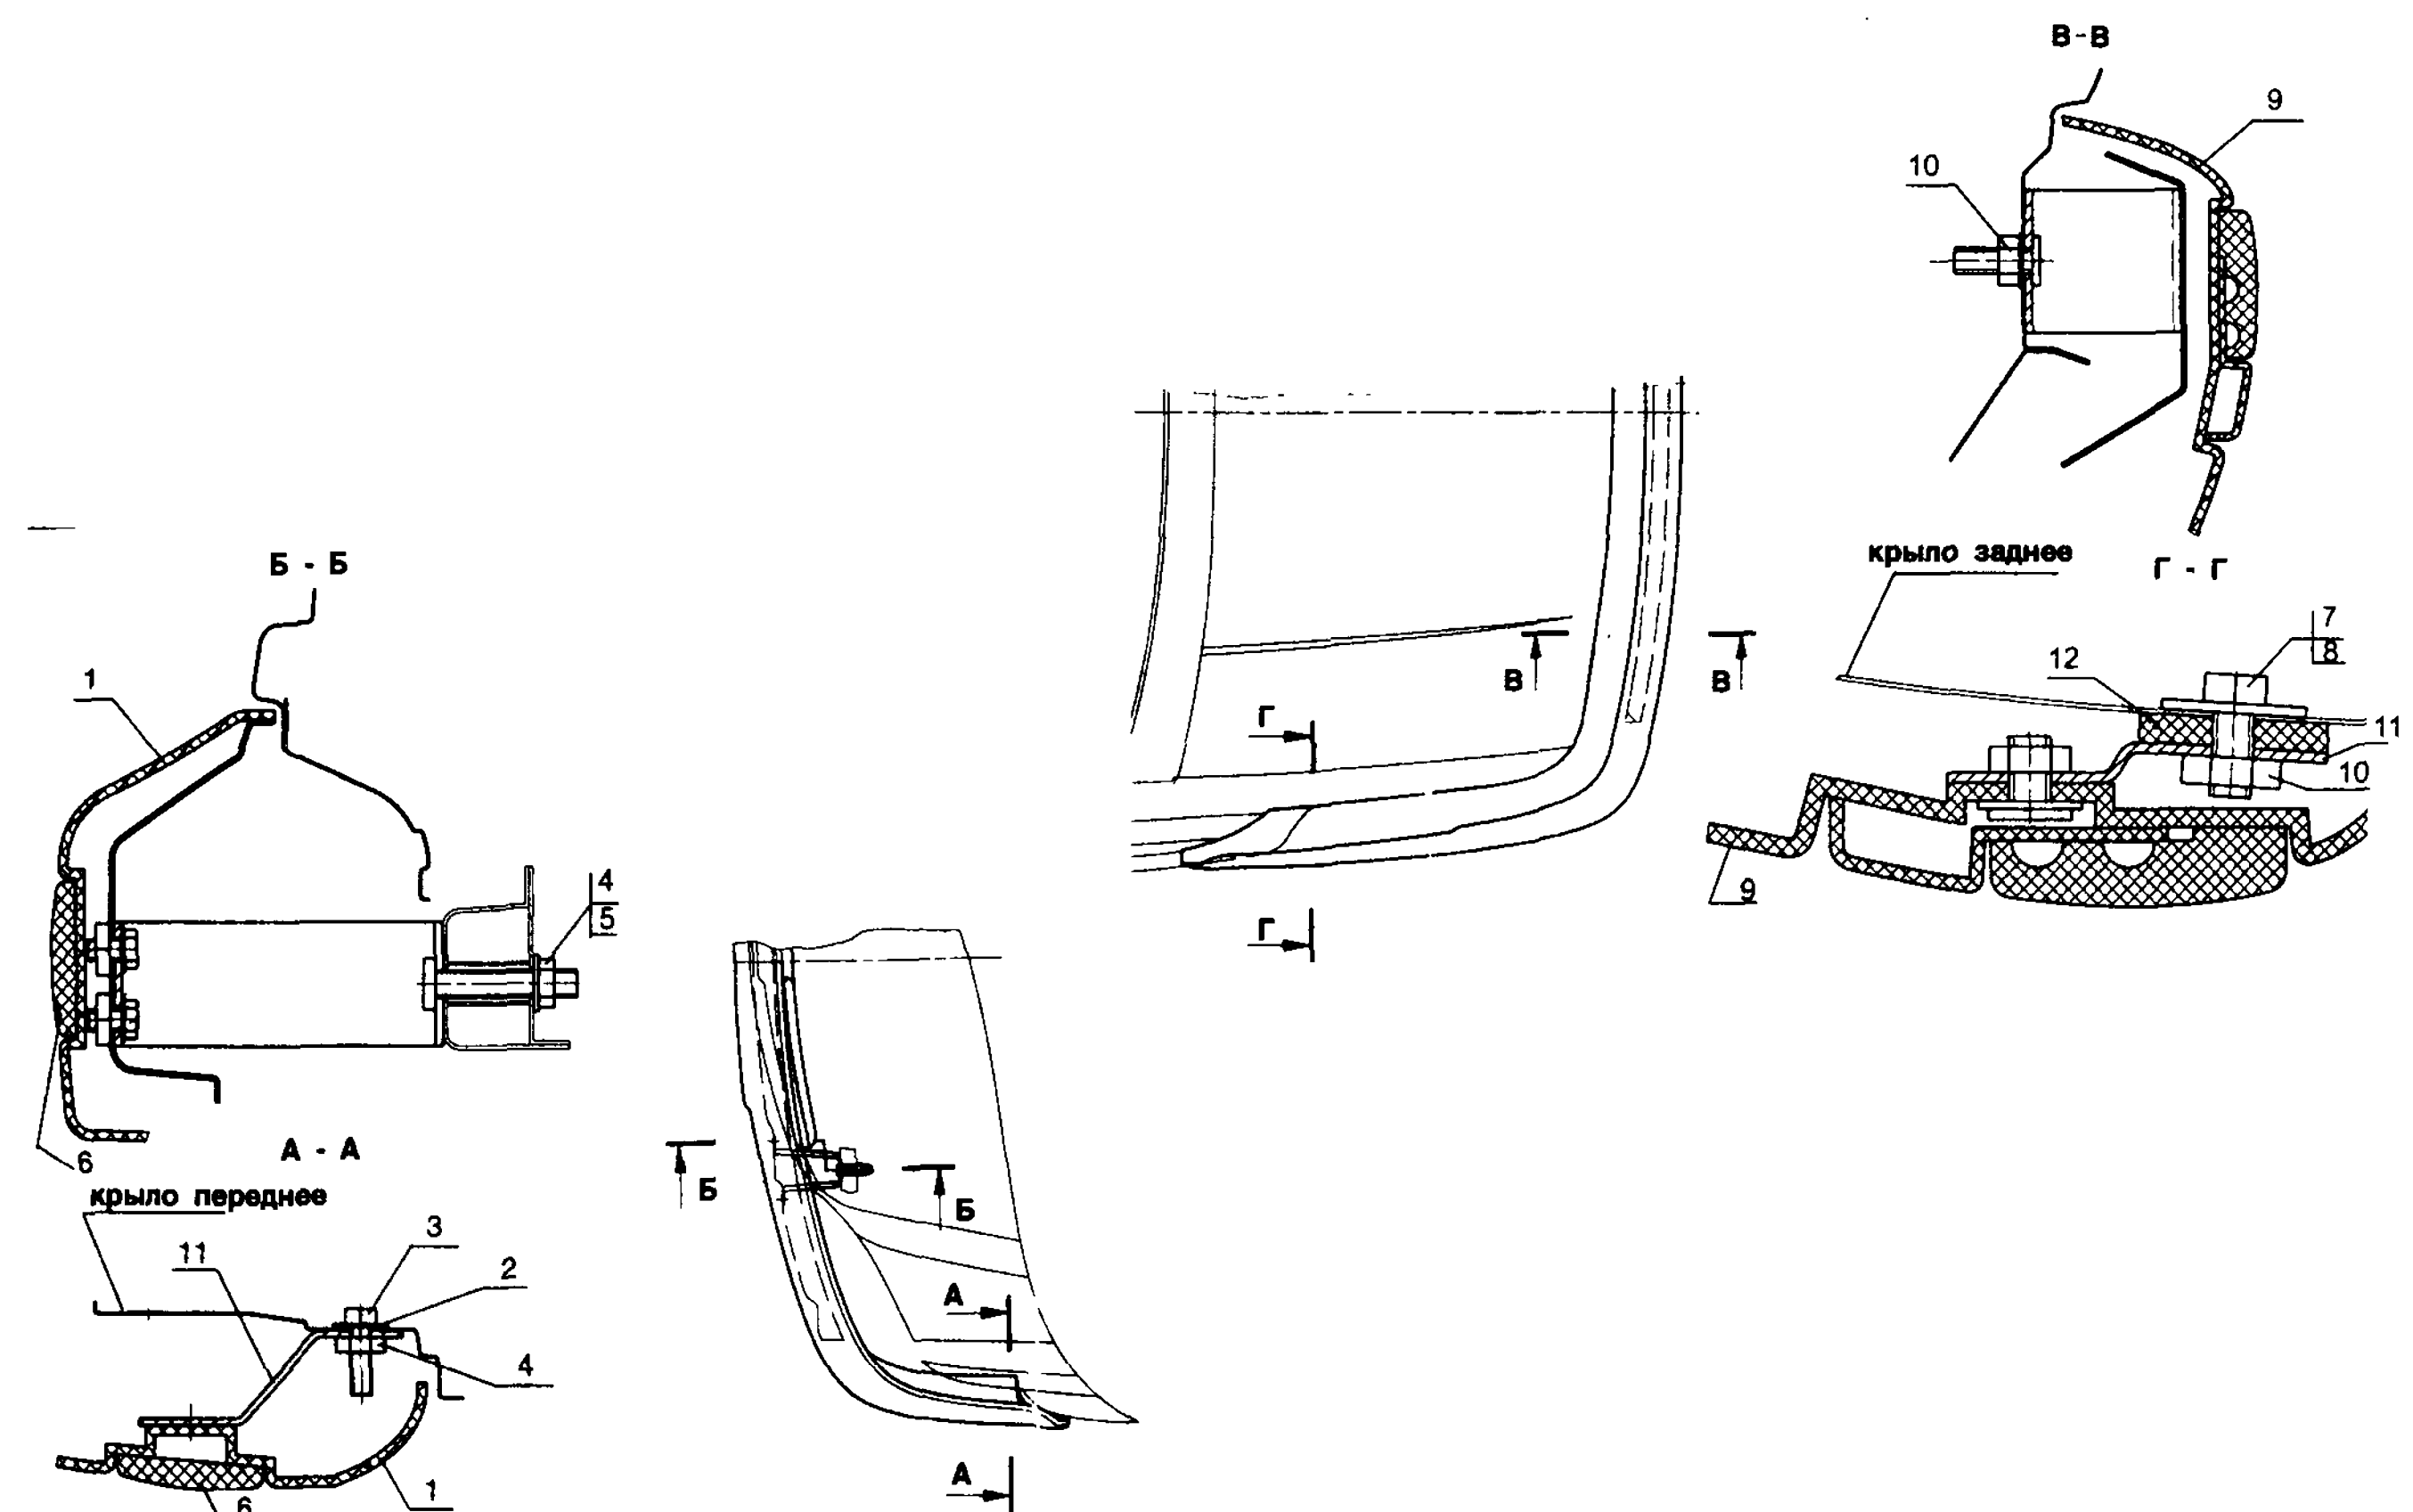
Передний и задний буфер: 1 - передний буфер; 2 - шайба; 3 - болт; 4 - гайка; 5 - шайба; 6 - накладка буфера; 7 - болт; 8 - шайба; 9 - задний буфер; 10 - гайка; 11 - шайба; 12 - резиновый буфер
